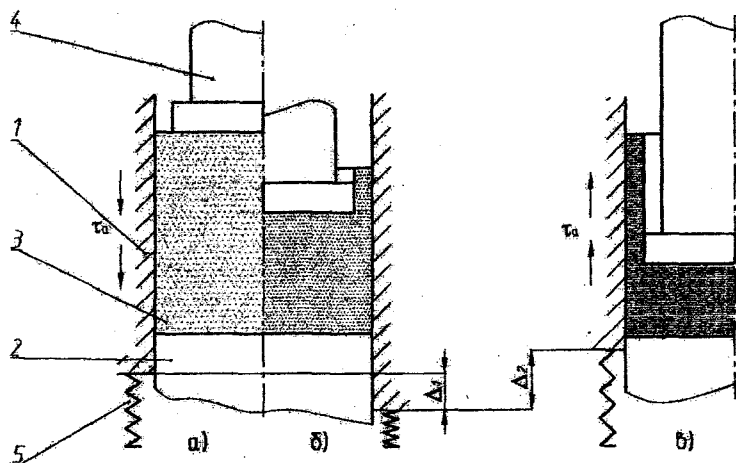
Схема уплотнения порошковой заготовки в плавающей матрице: а) осадка; б) начало выдавливания; в) окончание выдавливания; 1 - матрица; 2 - нижний пуансон (выталкиватель); 3 - спеченная порошковая заготовка; 4 - пуансон; 5 - пружина, расположенная под нижним торцом
